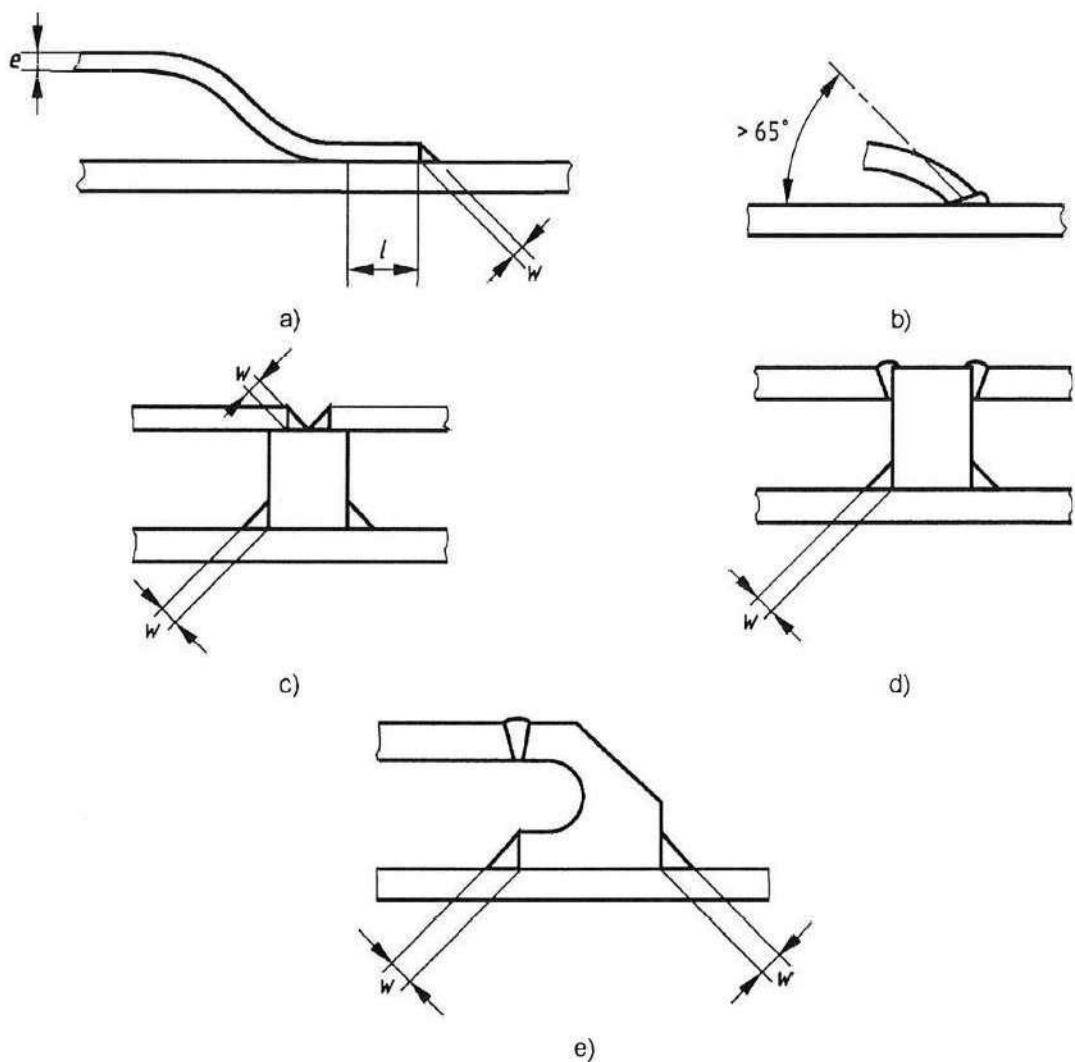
Типовое присоединение топочных каналов к корпусам
